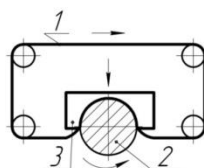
Схема шліфування абразивною стрічкою:
